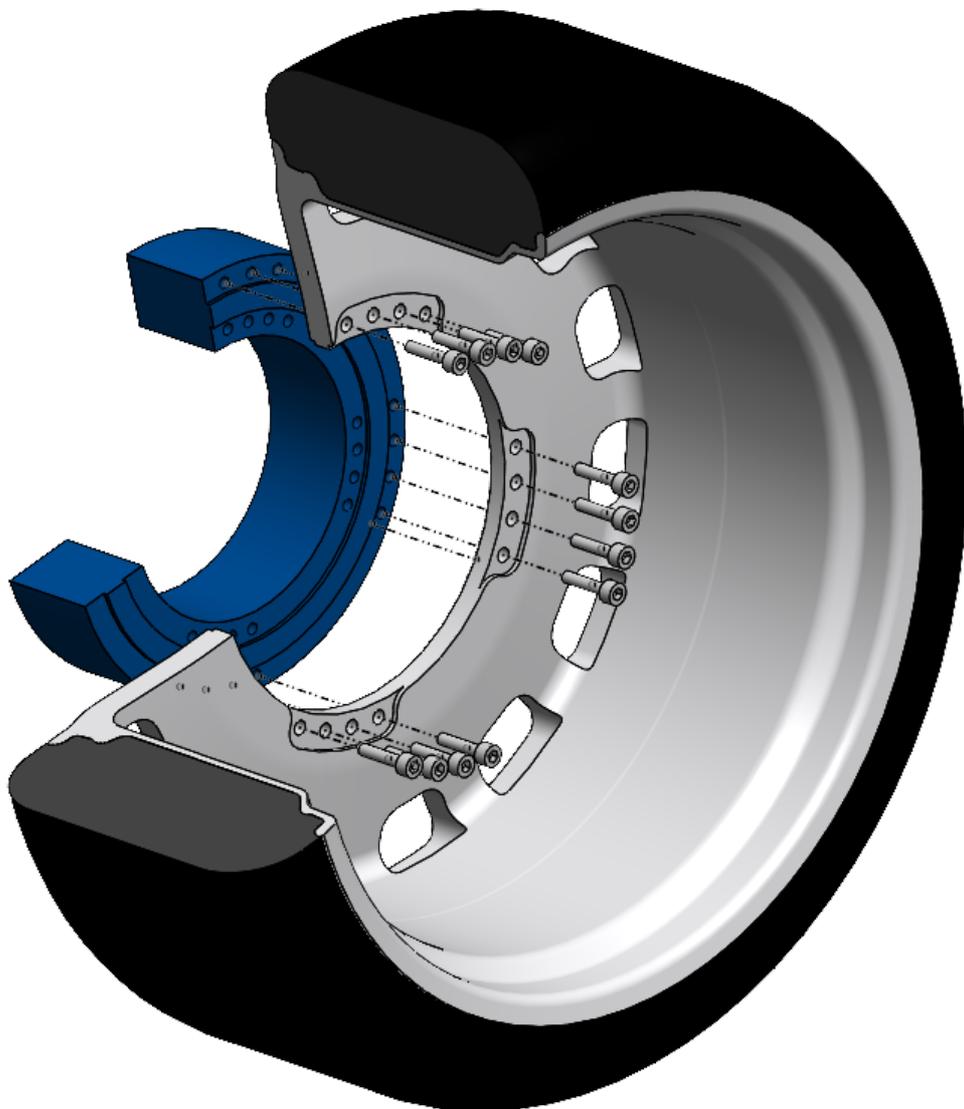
Die modifizierte Felge (= Außenadapter) mit dem WFT (blau) verschrauben.
